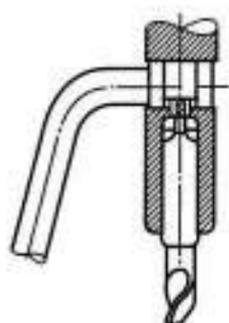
Эксцентриковый ключ для удаления режущего инструмента из шпинделя станка
